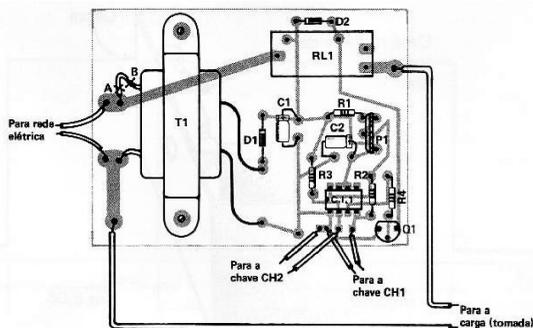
Distribuição dos componentes na plaqueta de circuito impresso. Observar que o chanfro do integrado situa-se à esquerda do leitor.
